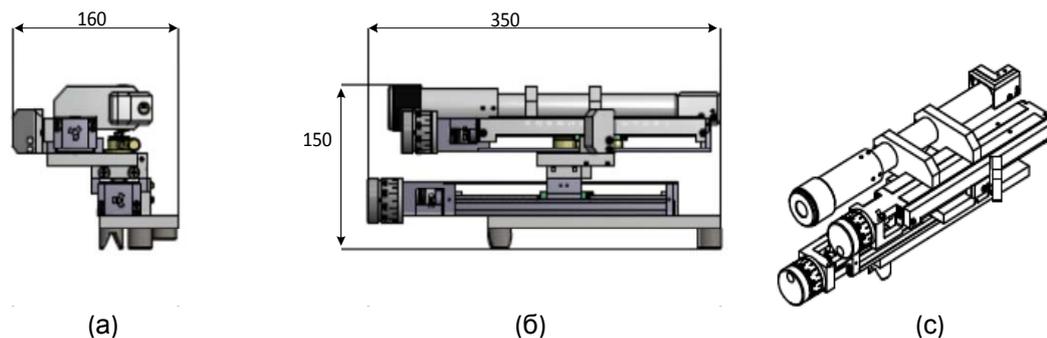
Транспортное положение ОМК-130-02, габаритные размеры
